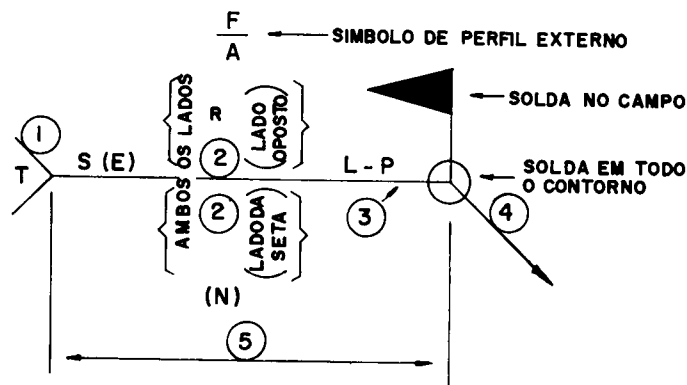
Localização dos elementos no símbolo de soldagem
